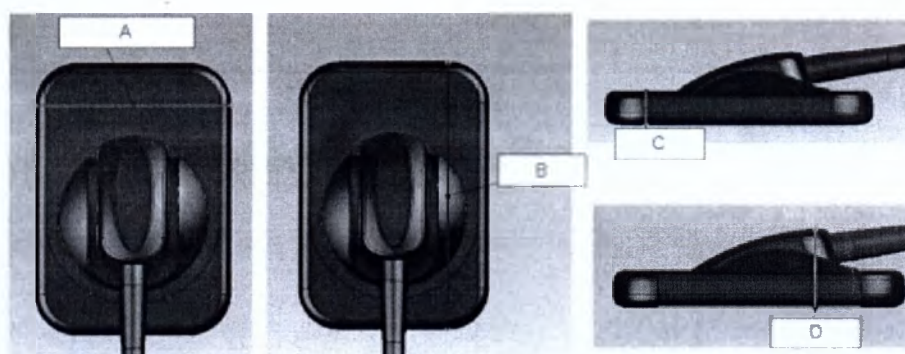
Внешний вид и габаритные размеры датчиков
